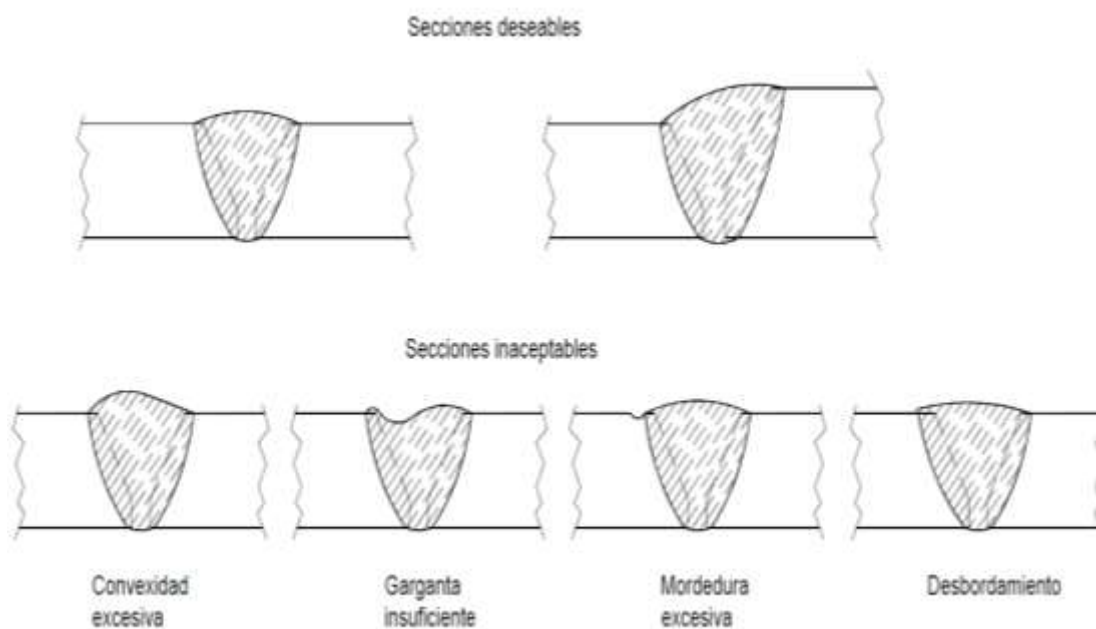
Defectos de Forma en Soldaduras a Tope
